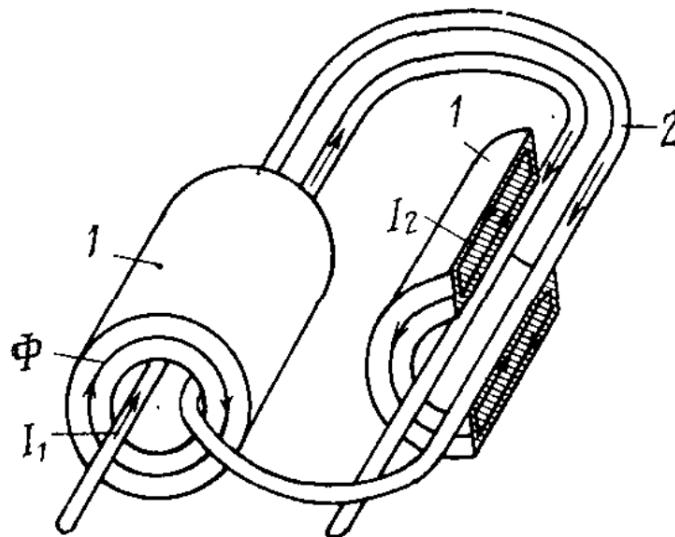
Багатовитковий індуктор у феромагнітній трубці:
